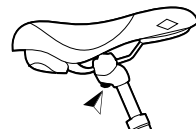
Sattelstütze mit nur einer Klemmschraube
